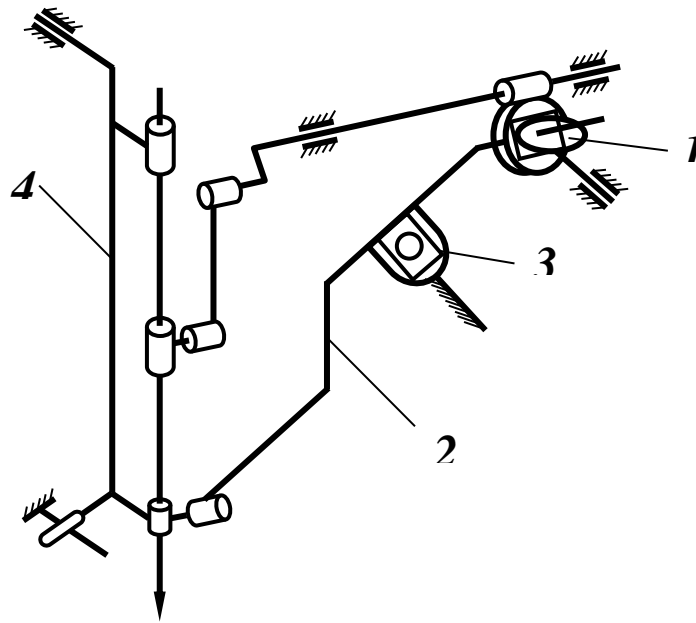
г – Конфигурация кривошипно-ползунного механизма иглы, расположением шатуна наверху главного вала: 1 - кулачок; 2 – рычага вилка; 3 - кулиса; 4 - рамка игловодителя
